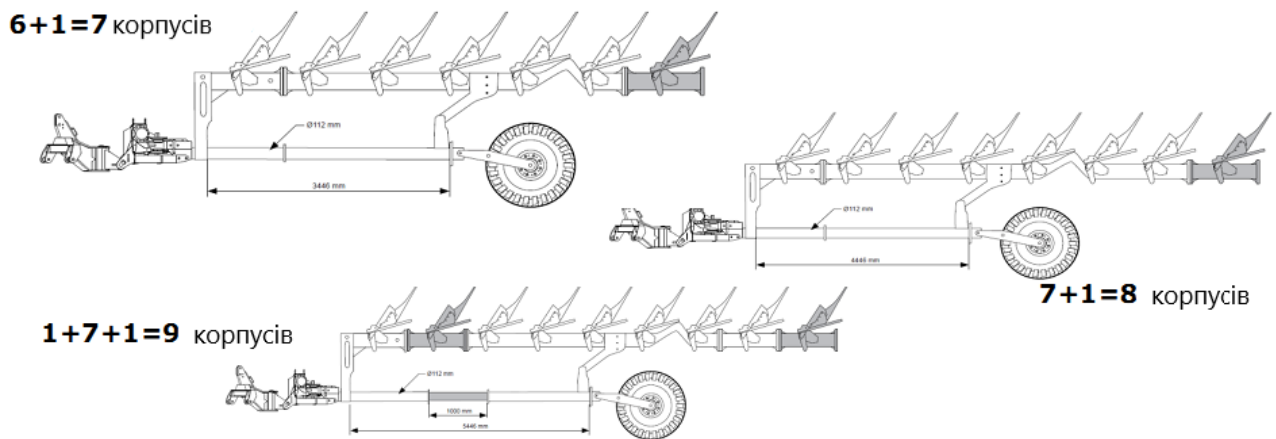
Моделі з різною кількістю корпусів: 7 корпусів (6+1) та 8 корпусів (7+1)
